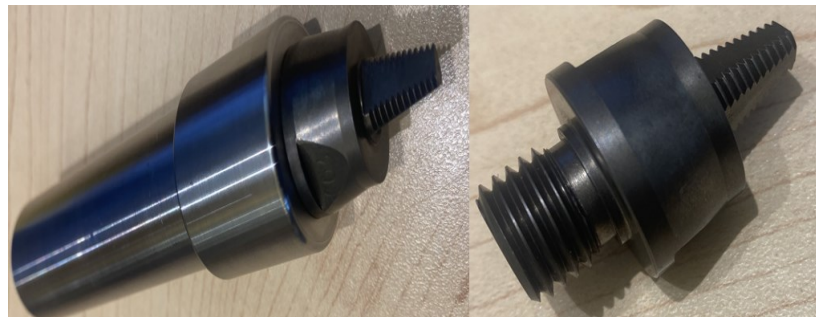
Outil à simple épaulement conique utilisé pour souder à recouvrement
